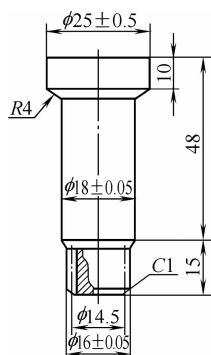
冷挤压中碳钢洗衣机齿轮轴
